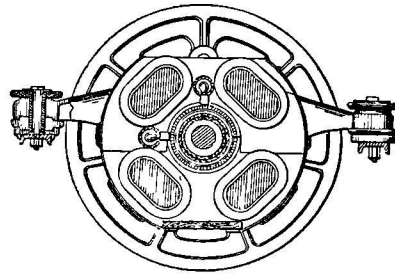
Moteur « gearless » Short, premier type. — Coupe transversale.
